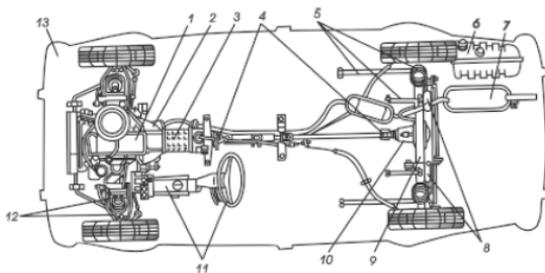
Общая компоновка заднеприводного автомобиля ВАЗ 2105 с расположением двигателя спереди: 1 – двигатель; 2 – сцепление; 3 – коробка передач; 4 – карданная передача; 5 – детали задней подвески; 6 – топливный бак; 7 – глушитель; 8 – амортизаторы; 9 – задний мост; 10 – главная передача и дифференциал; 11 – рулевое управление; 12 – детали перед-
